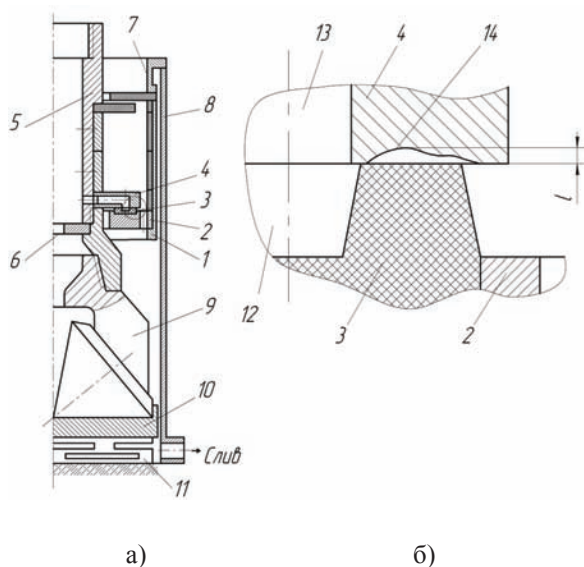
а – принципиальная схема стенда для испытаний осевых подшипников забойного двигателя, б – выделенный элемент гидростатического резинометаллического подшипника
